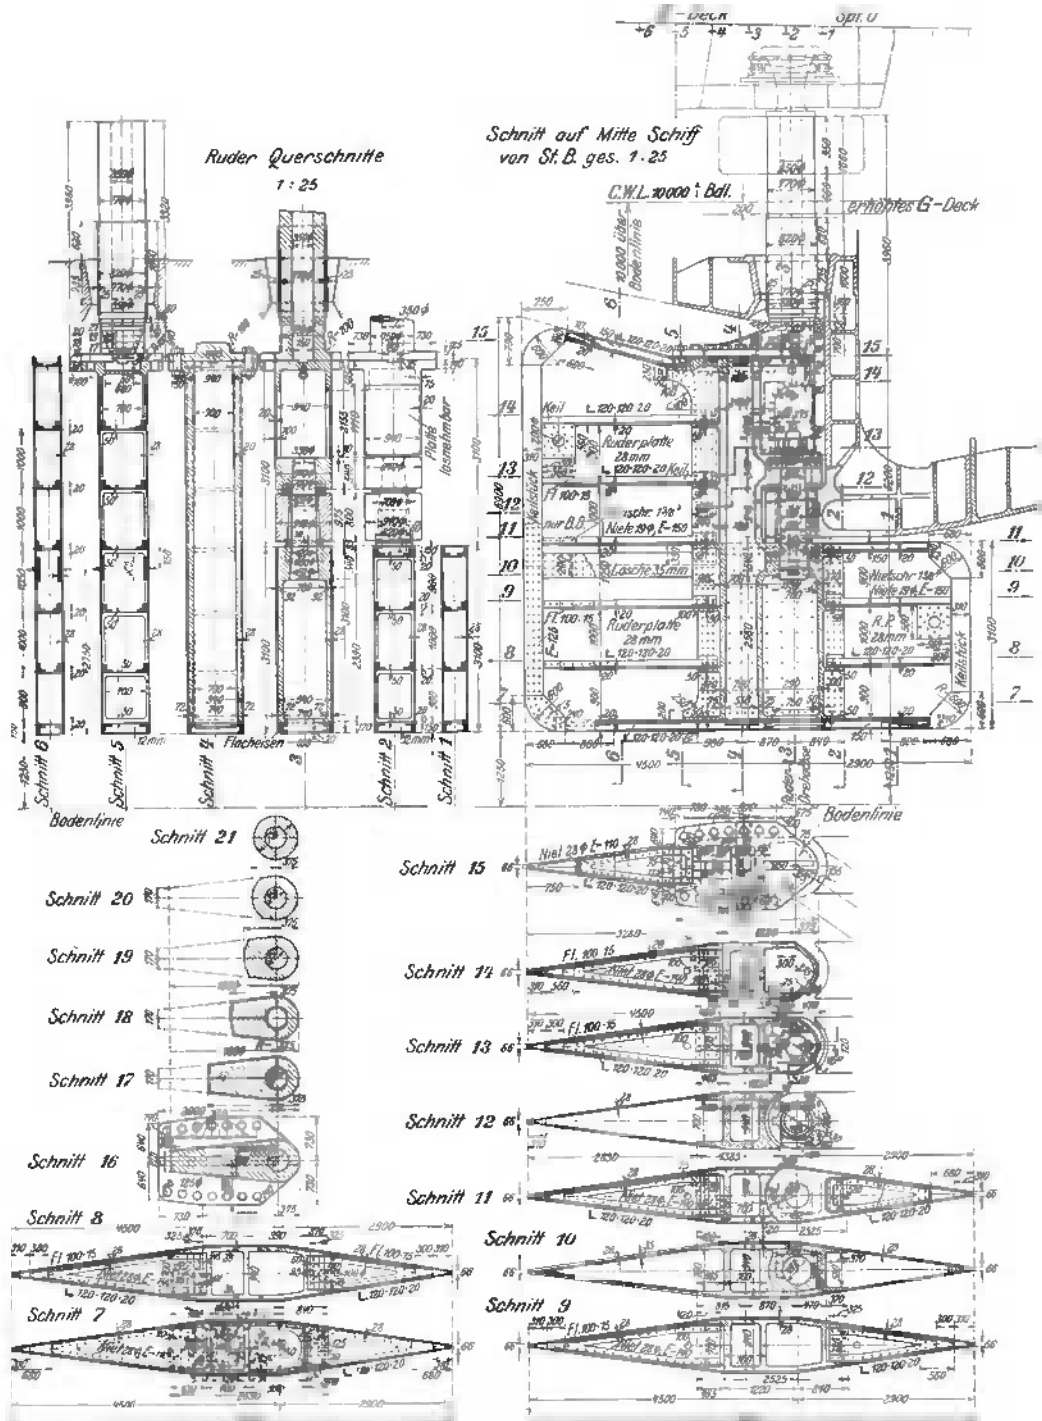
Balanceruder für den Vierschrauben-Schnelldampfer „Europa“.
